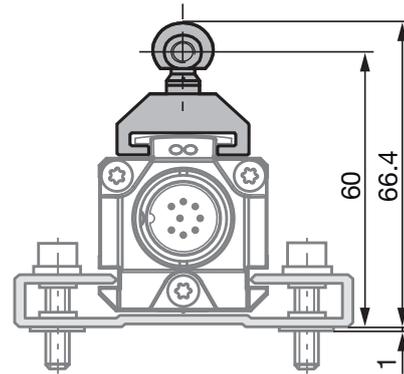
Maße und Abstände mit Positionsgewerber BTL5-F-2814-1S
